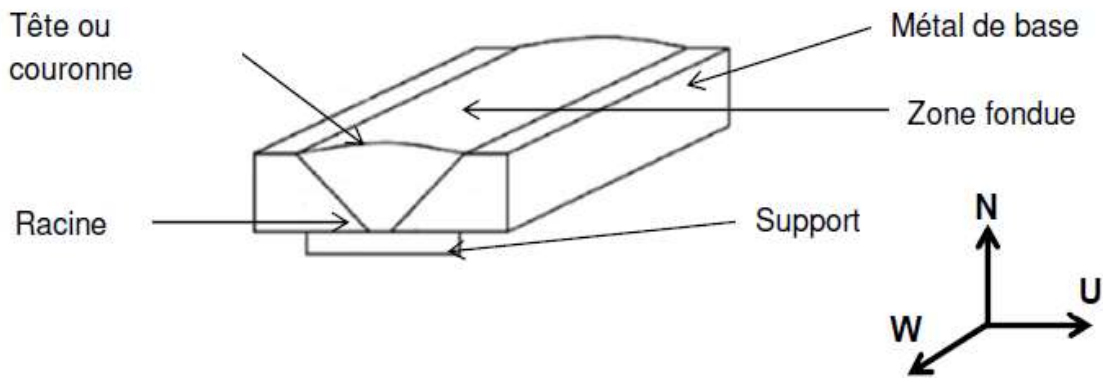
Schéma d'un assemblage soudé par une simple passe [8].
